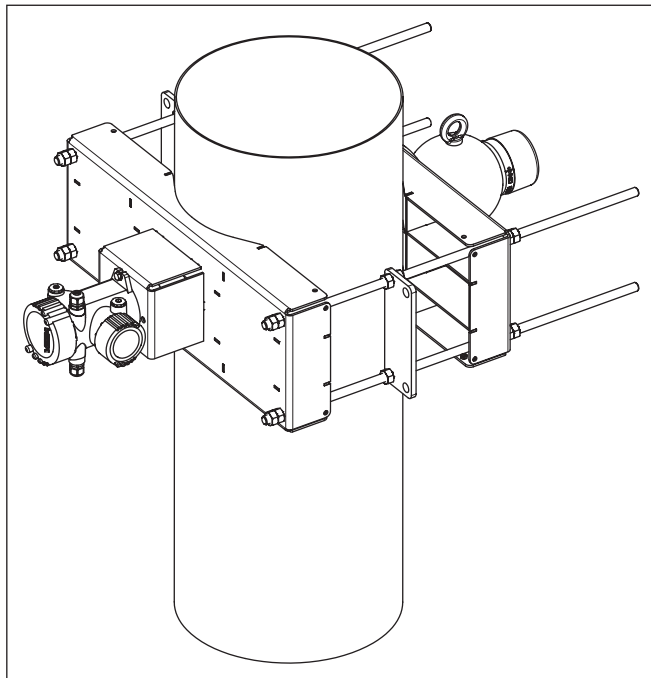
Dispositivo de sujeción con sensor montado horizontalmente
